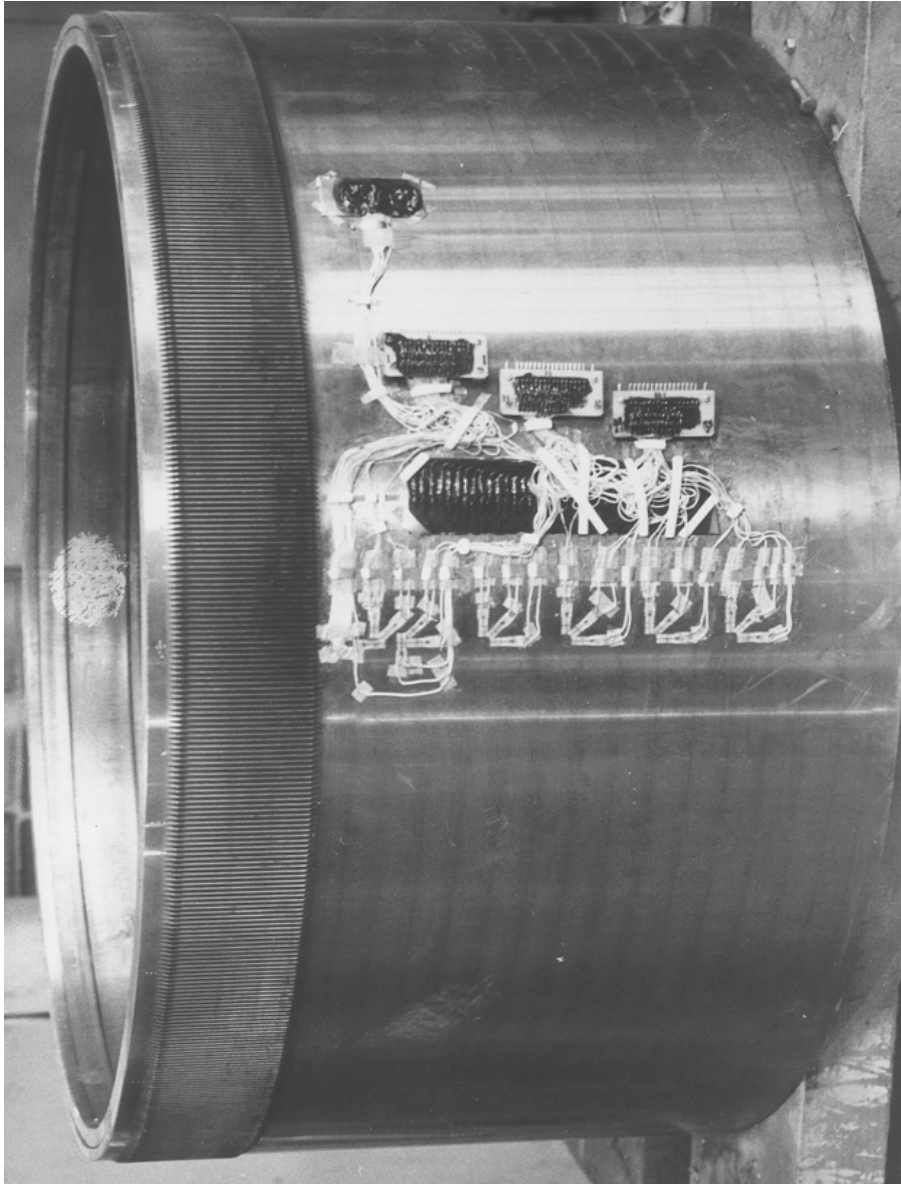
Гибкое зубчатое колесо волнового редуктора привода наклона передвижного миксера МП – 600 АС с тензорезисторами, смонтированными на упругой цилиндрической оболочке
